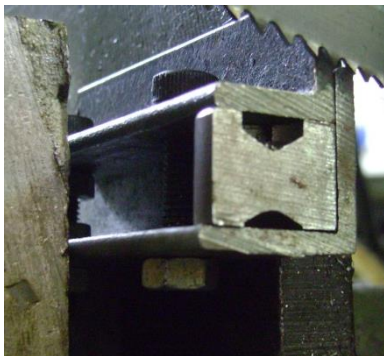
Fixação dos corpos de prova na máquina de serra fita.
